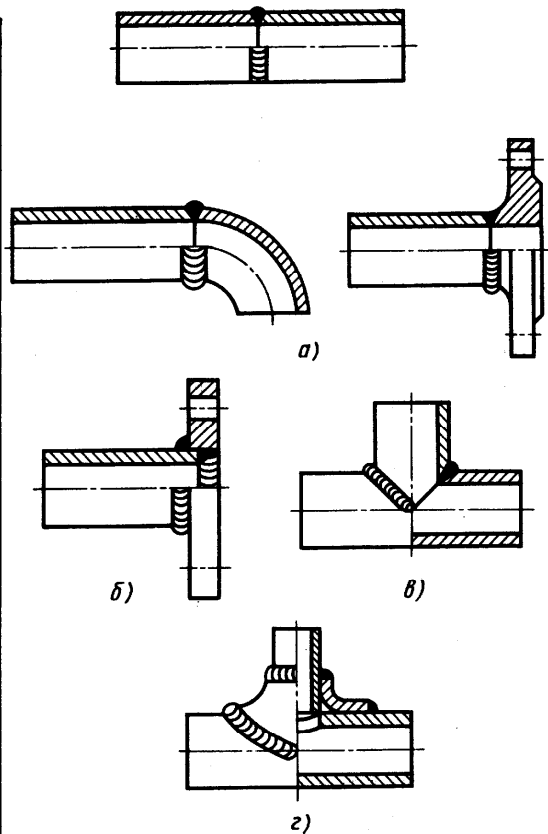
Типы сварных соединений, применяемых при изготовлении и монтаже трубопроводов
